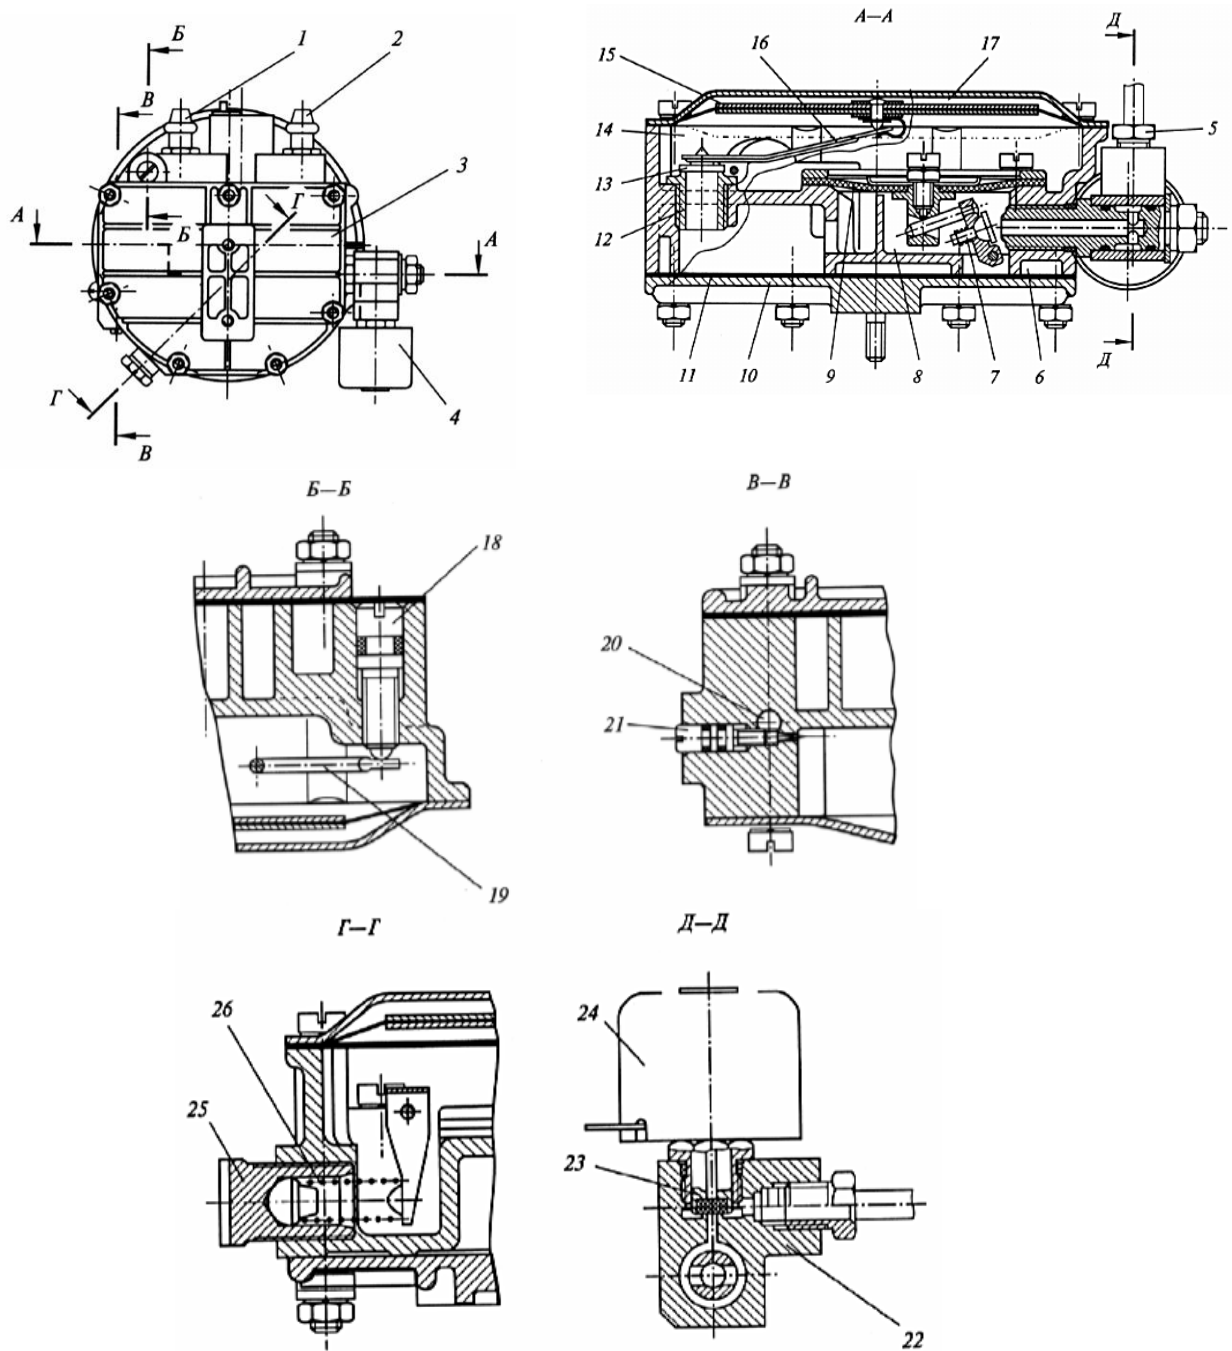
Конструкция редуктора-испарителя низкого давления ЗАО «Автосистема»:
